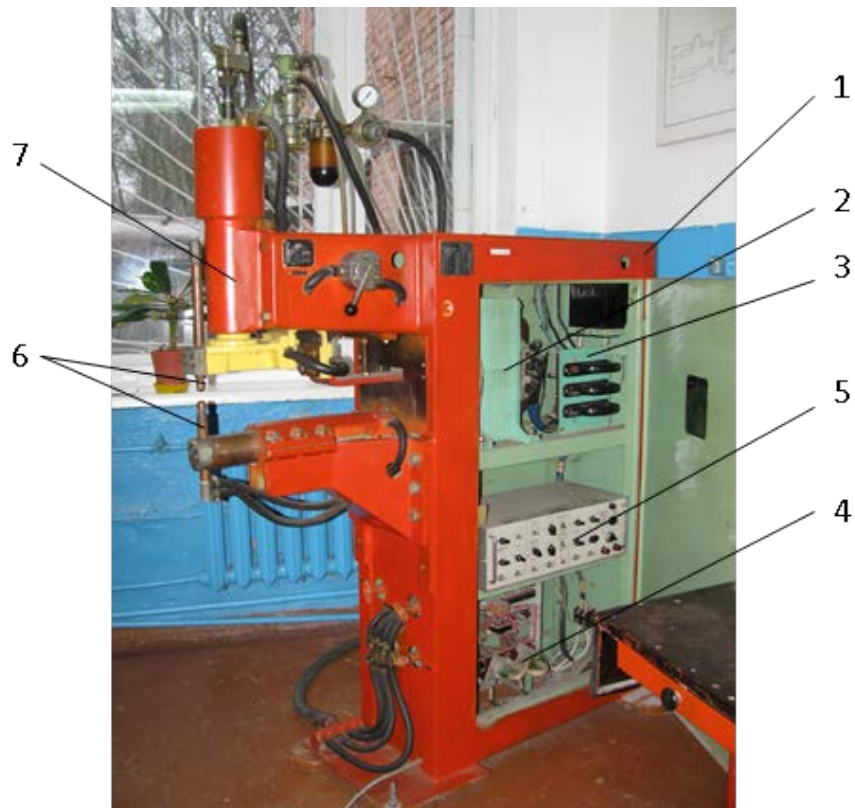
Загальний вигляд машини для електроконтактного точкового зварювання МТ-1216
